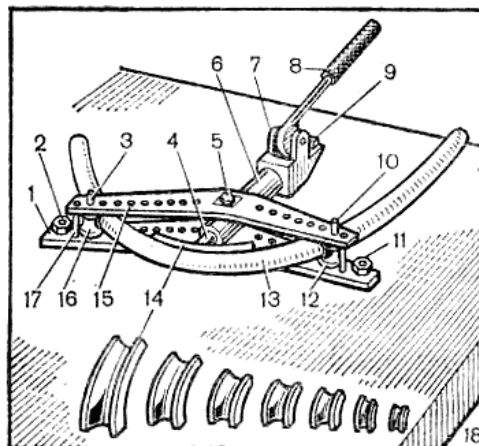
Станок для гибки труб с наполнителем – песком
